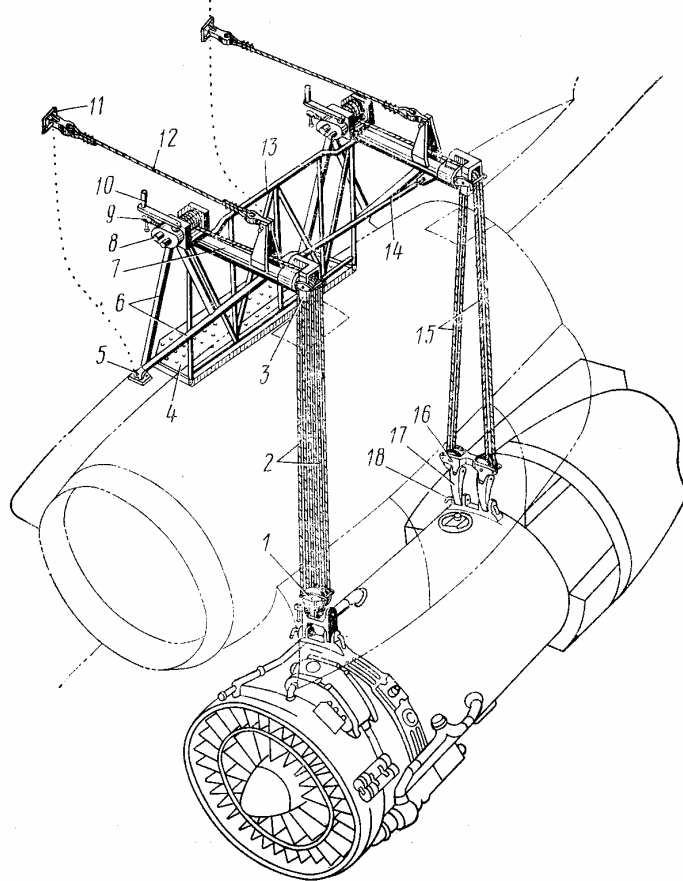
Приспособление 154.00.9960.070 для монтажа внешних двигателей:
